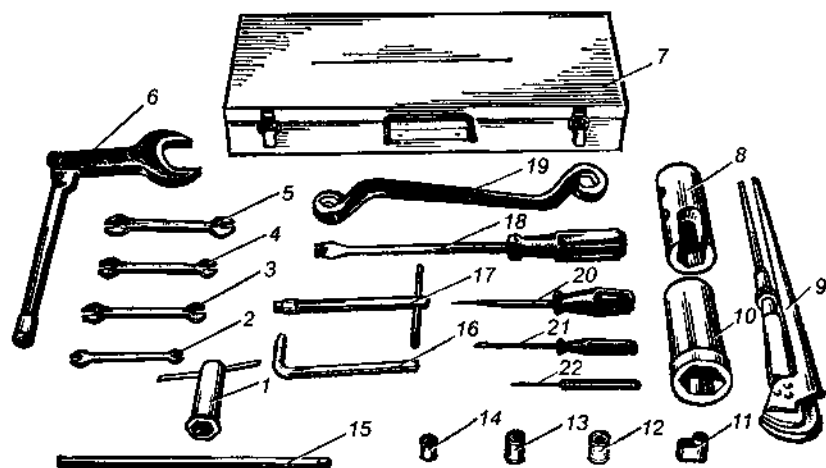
Комплект инструментов И-139: 1 — ключ для регулирования редуктора; 2, 3, 4, 5, 9, 18, 21 — стандартные инструменты; 6 — специальный ключ; 7 — футляр; 8 — ключ для вентилей баллона; 10 — торцевой специальный ключ; 11 — шпильковерт; 12 — торцевой ключ для крепления генератора; 13, 14 — торцевые ключи для крепления стартера; 15 — вороток; 16 — малая ручка; 17 — малая шарнирная ручка; 19 — ключ для гаек трубопроводов; 20 — квадратное шило; 22 — оправка седла клапана контрольного вентиля
